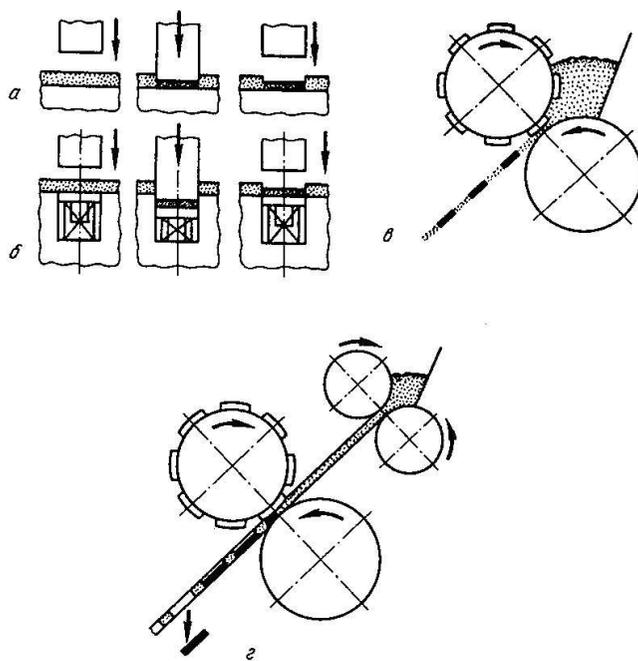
Схемы формирования плоских заготовок из высокопористой ленты между плитой и пуансоном (а), в штампе (б), непосредственно из порошка (в) и с формирующими вставками в валке (г)
